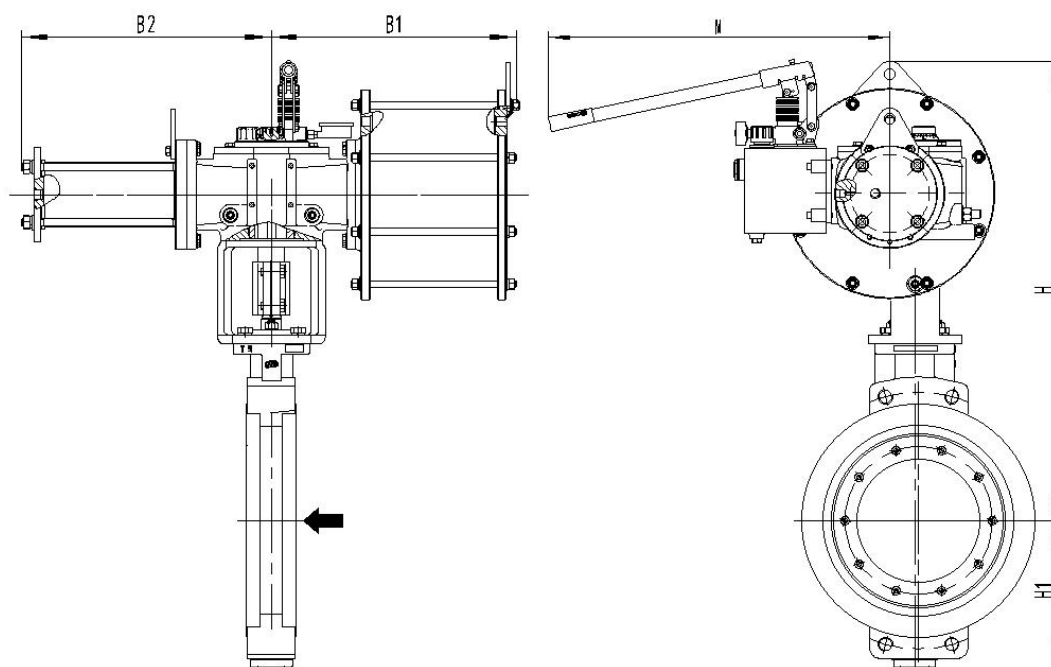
AW40D004~AW90D007 带液压手轮外形尺寸图
